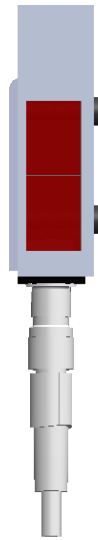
Vista frontal. Diseño del montaje de sensor y tope.
